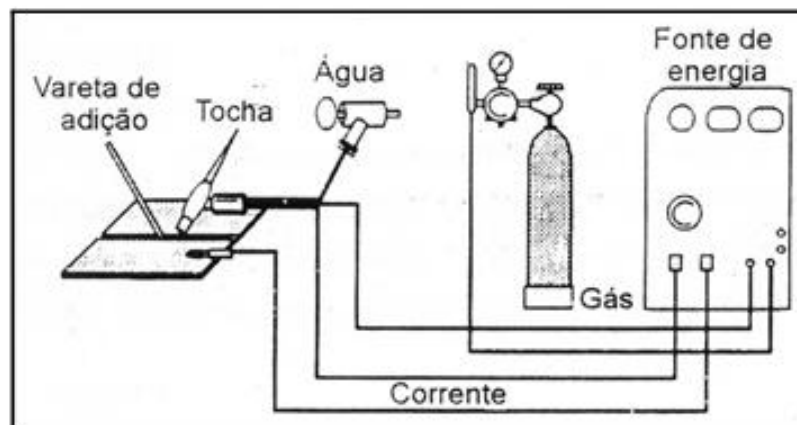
Equipamento básico para soldagem TIG (esquemático).
